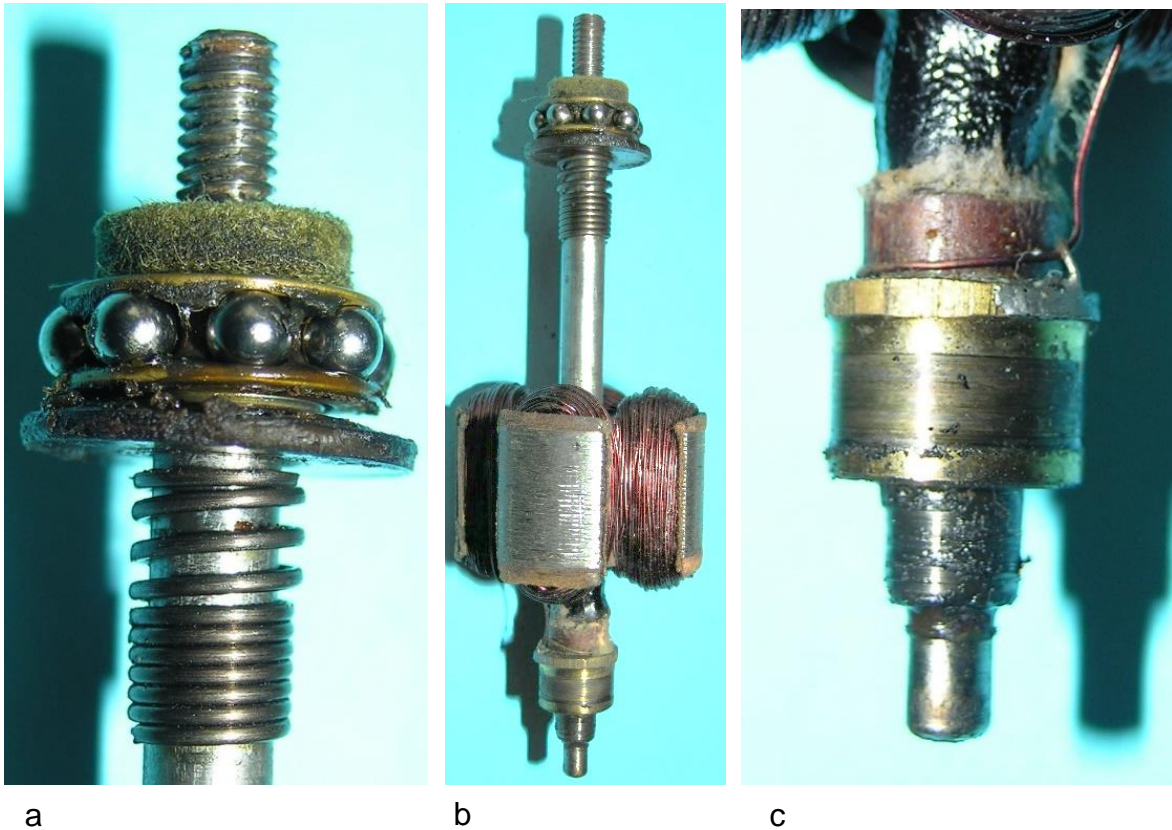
Läufer und seine Lager: a) Kugellager im Lagerhals, b) Vollständiger Läufer, c) Schleifring und Wellenende
